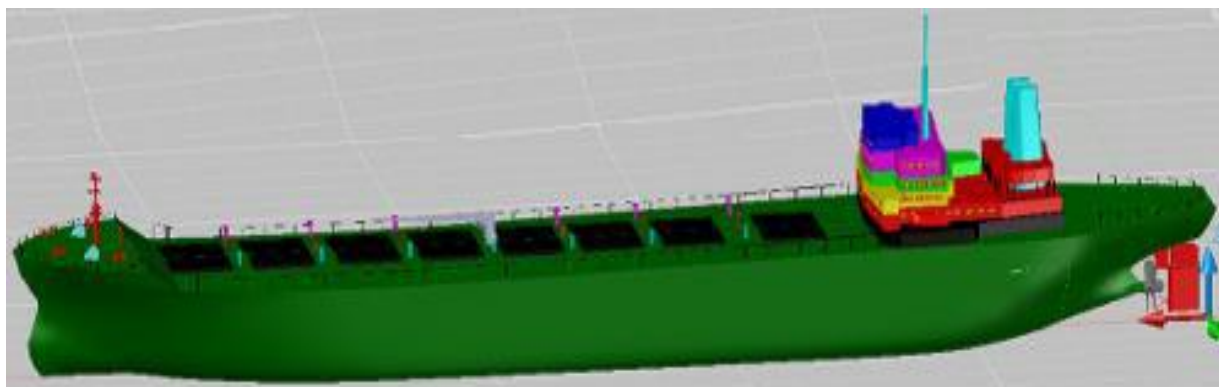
Общий вид корпуса с надстройкой в AutoCAD
